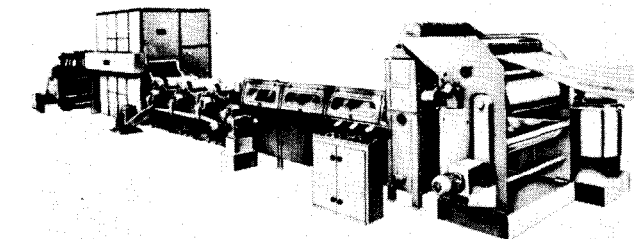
Gesamtansicht einer ILMA-Kontinue-Kammzugfärbeanlage mit Bobinenwickelmaschine am Auslauf
